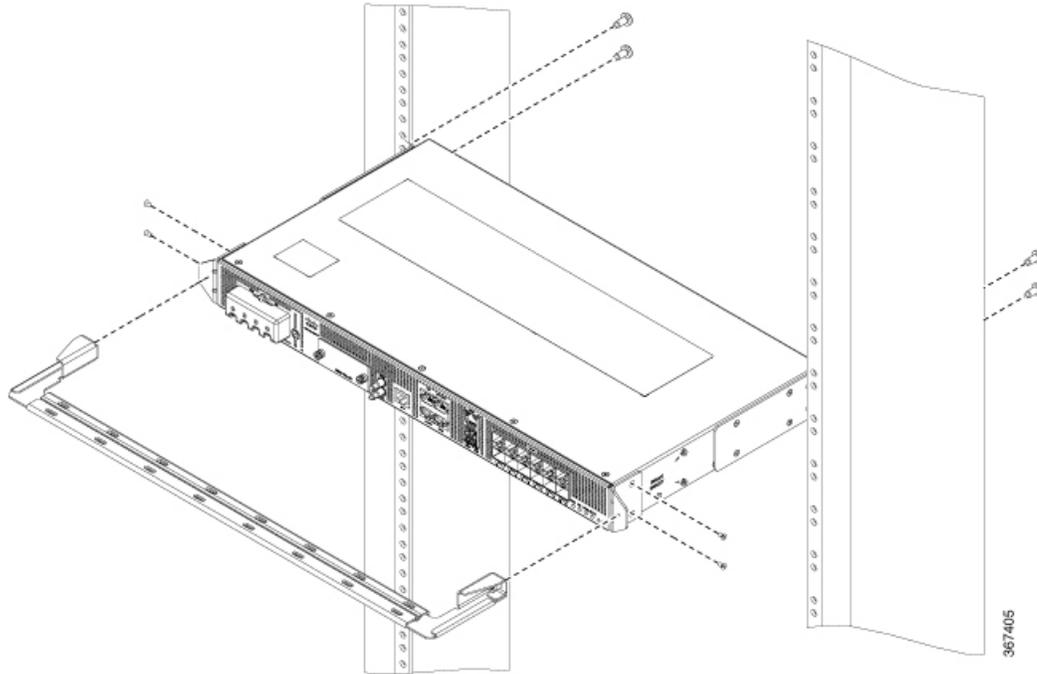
Dispositif de fixation avant avec guide-câble sur un rack de 21 pouces
